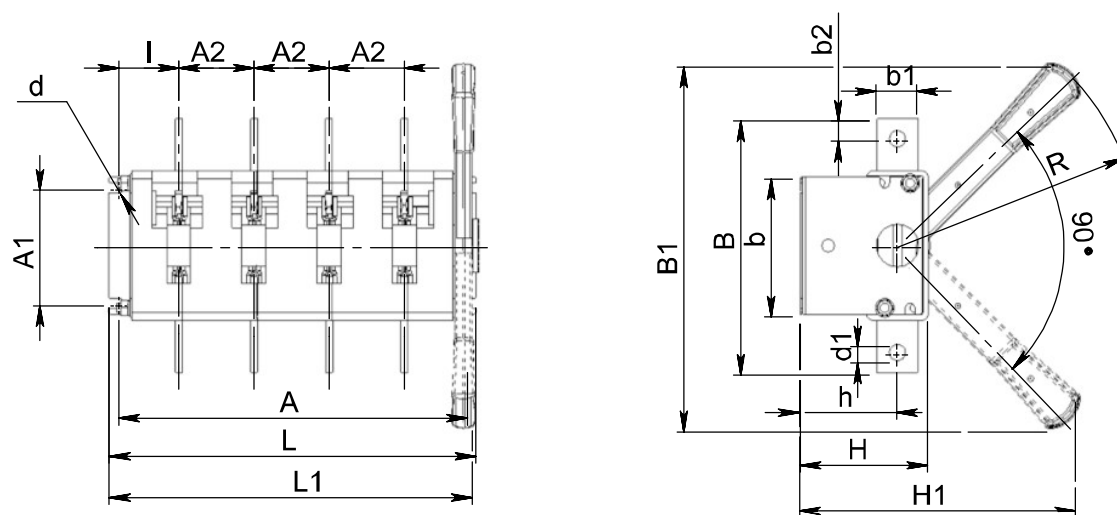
Выключатель-разъединитель на одно направление 4-полюсный с боковой ручкой
